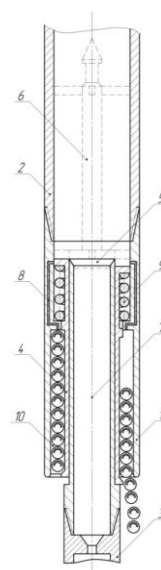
Забойный шаропитатель: 1 – корпус; 2 – колонна буровых труб; 3 – ШЭБС; 4 – подвижный элемент; 5 – седло; 6 – запорный клапан; 7 – центральный канал; 8 – перепускной канал; 9 – пружина; 10 – отсек для размещения шаров
